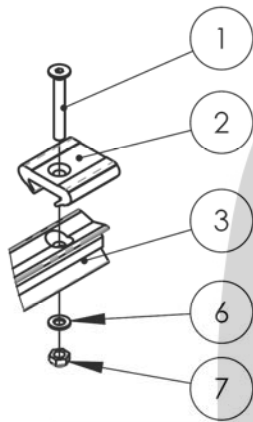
Montaje del anclaje final incluyendo el tope de final de carril
